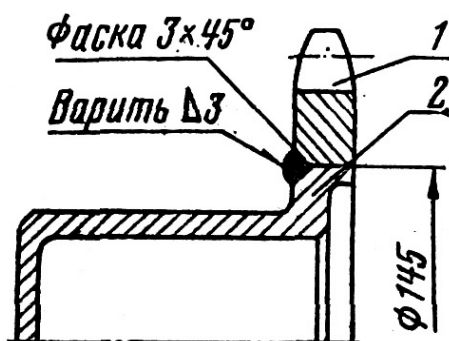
Ремонт ведомой зубчатки: 1 — новый венец (E=40 —.44); 2 — старая зубчатка (тормозной барабан)
